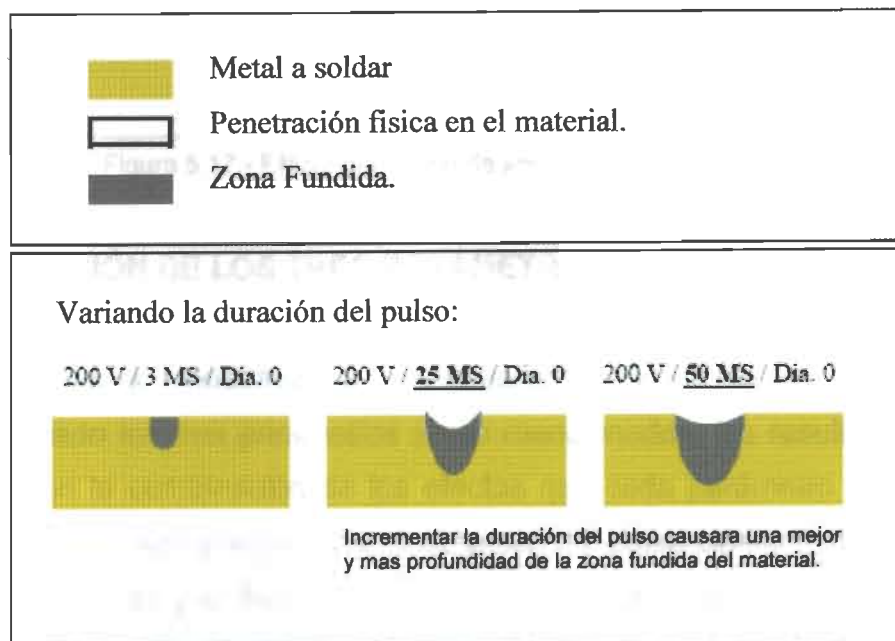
Efecto de la duración del pulso en la soldadura láser.
